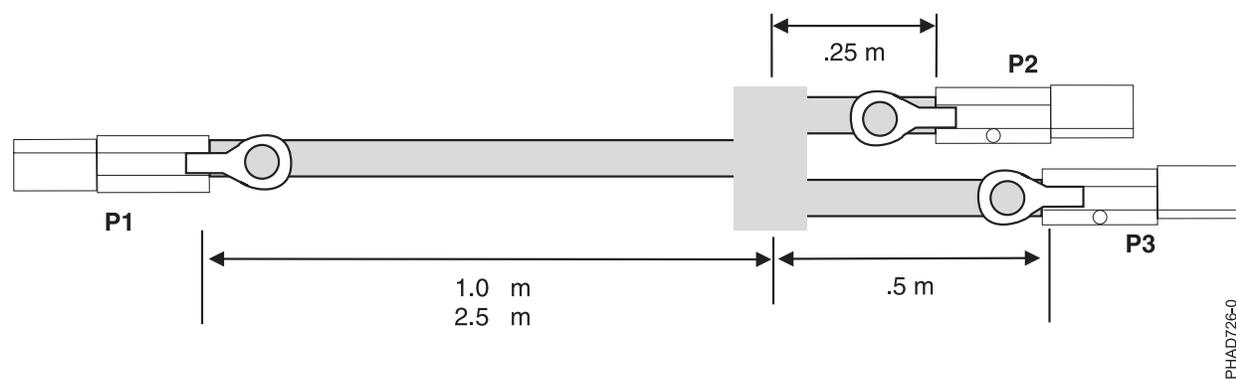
Comprimentos de cabo do conjunto de cabos externos SAS YI
